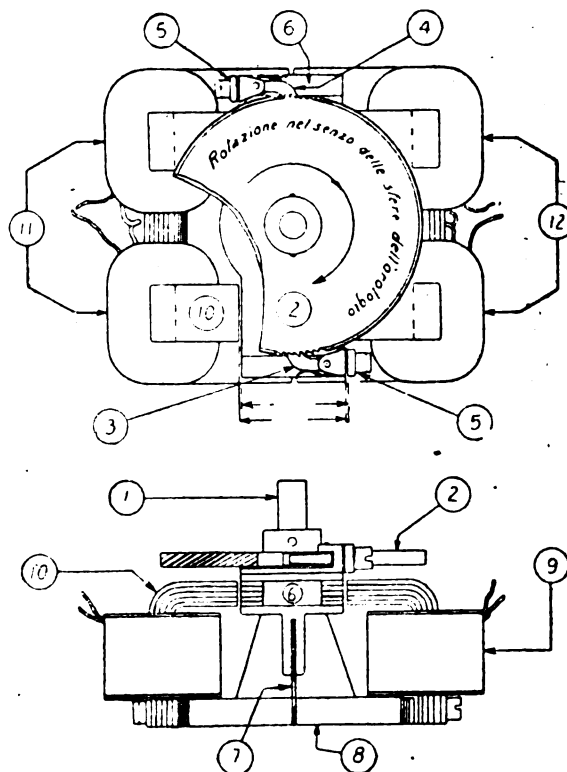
Vista d'insieme del piccolo motore elettromagnetico.
